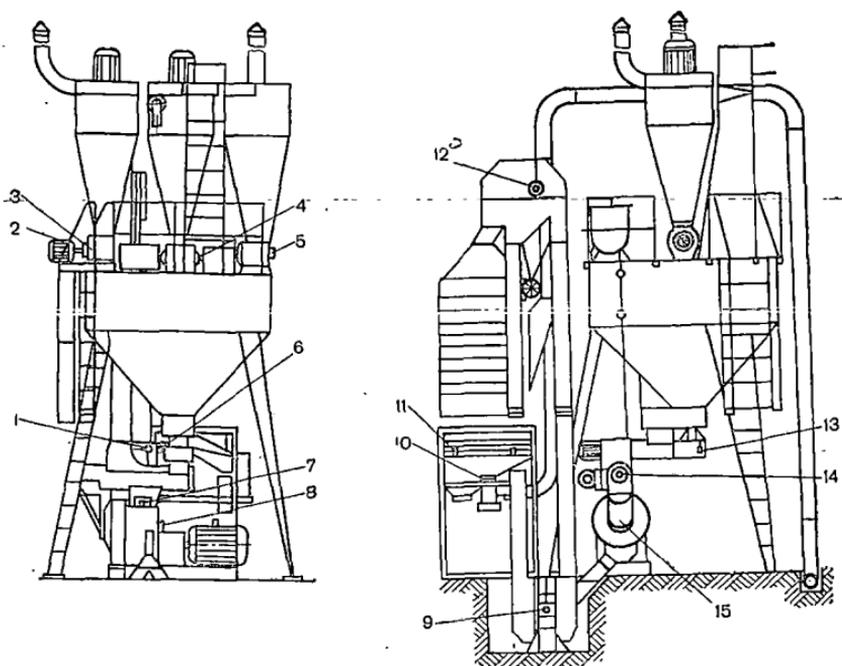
Схема смазки оборудования для гранулирования ОГМ-1,5: 1 — редуктор привода дозатора; 2 — мотор-редукторы привода шлюзовых затворов и норин; 3, 4, 5 — подшипники шлюзовых затворов; 6 — подшипник натяжной звездочки привода дозатора; 7 — редуктор пресса; 8 — подшипники прессующих валцов; 9, 12 — подшипники норин; 10 — подшипники приводного вала сортировки; 11 — эксцентриковые втулки на приводном валу сортировки; 13 — конический редуктор привода сводоразрушителя в бункере; 14 — подшипник смесителя; 15 — подшипники питателя
